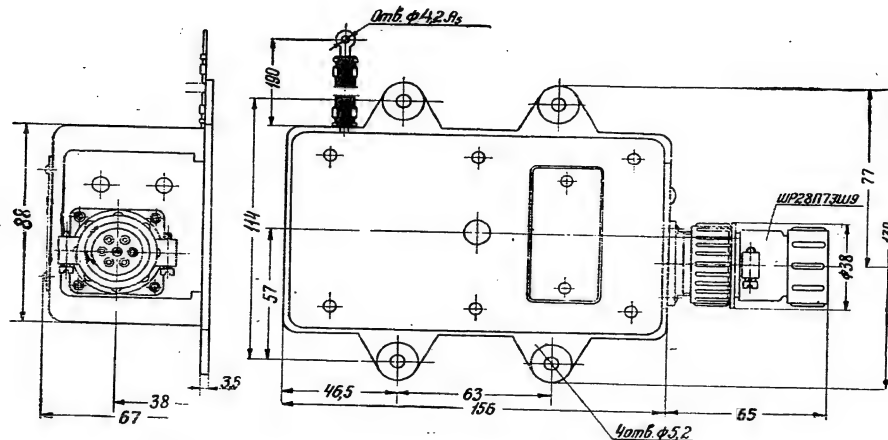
Габаритные размеры тиратронного прерывателя ПТ-56
